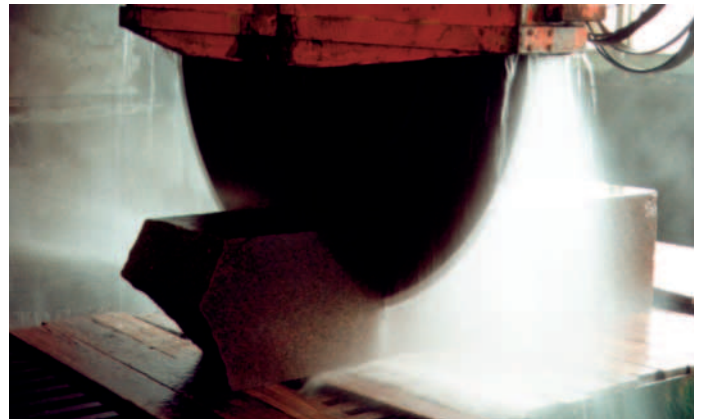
Großkreissäge mit Blattdurchmesser 1600 mm, POSTAER SANDSTEIN, Schnittlänge 300 mm [2].
